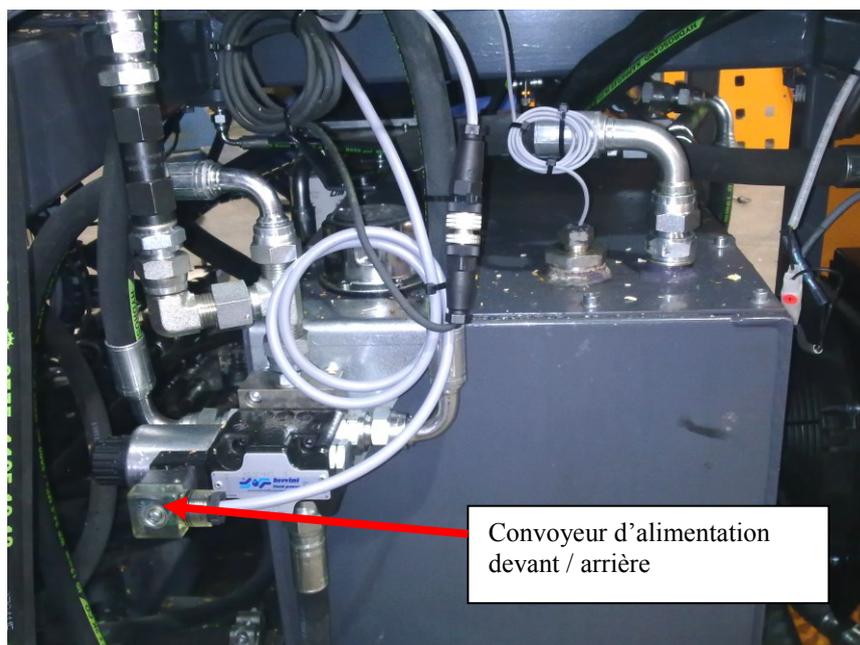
La soupape du contrôle du convoyeur d'alimentation (derrière de la machine à côté du
